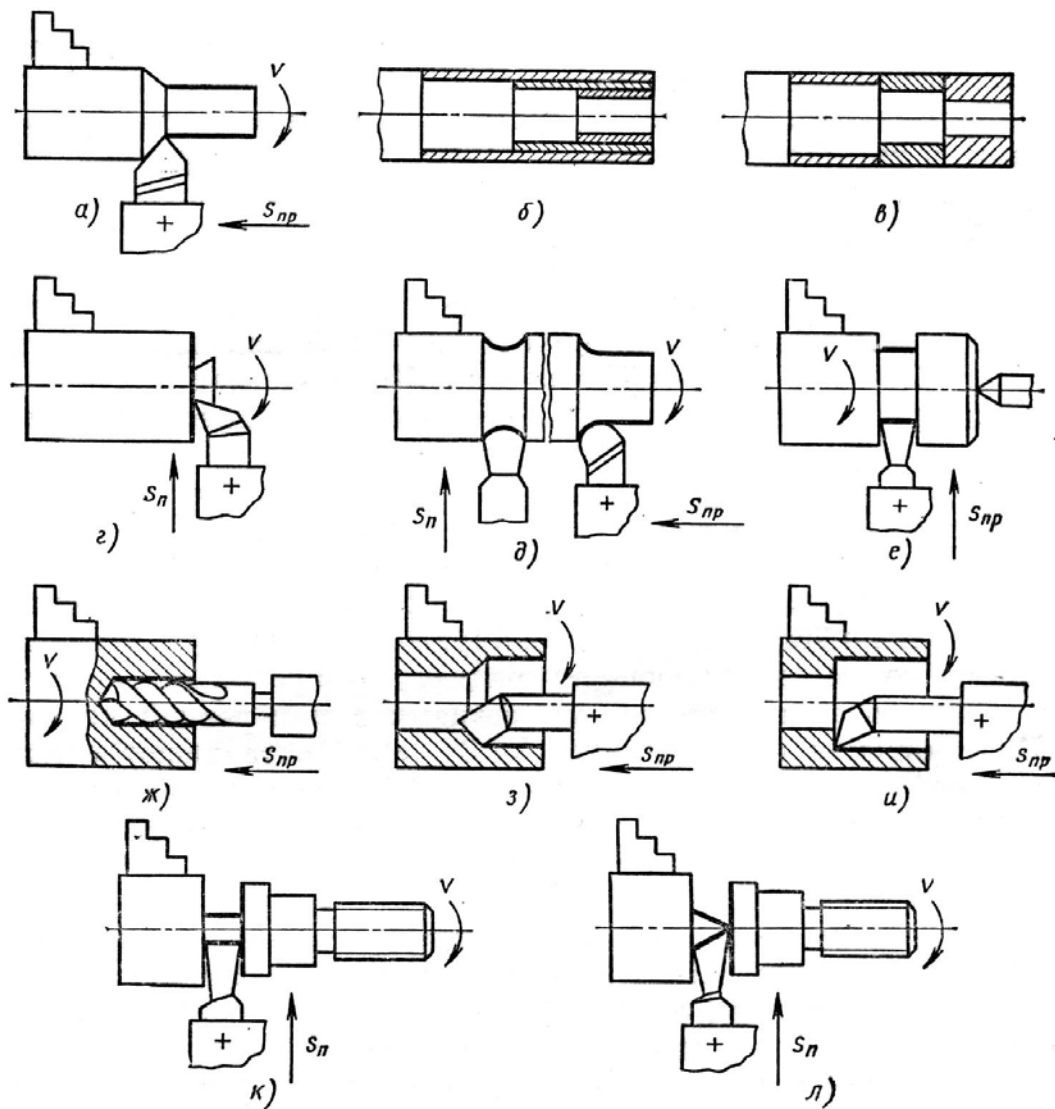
Схемы обработки заготовок на токарно-винторезном станке: а – обтачивание наружных цилиндрических поверхностей; б, в, – обтачивание ступенчатых валов; г – подрезание торцов; д – обтачивание галтелей и скруглений; е – протачивание канавок; ж – сверление отверстий; з, и – растачивание отверстий; к, л – отрезание обработанных заготовок
